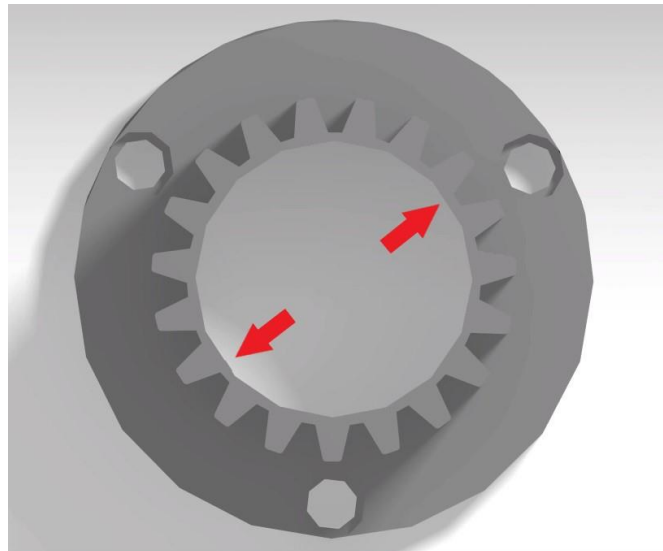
Vista en detalle del ESCARIADO_ACABADO del piñón (Fuente: elaboración propia)
